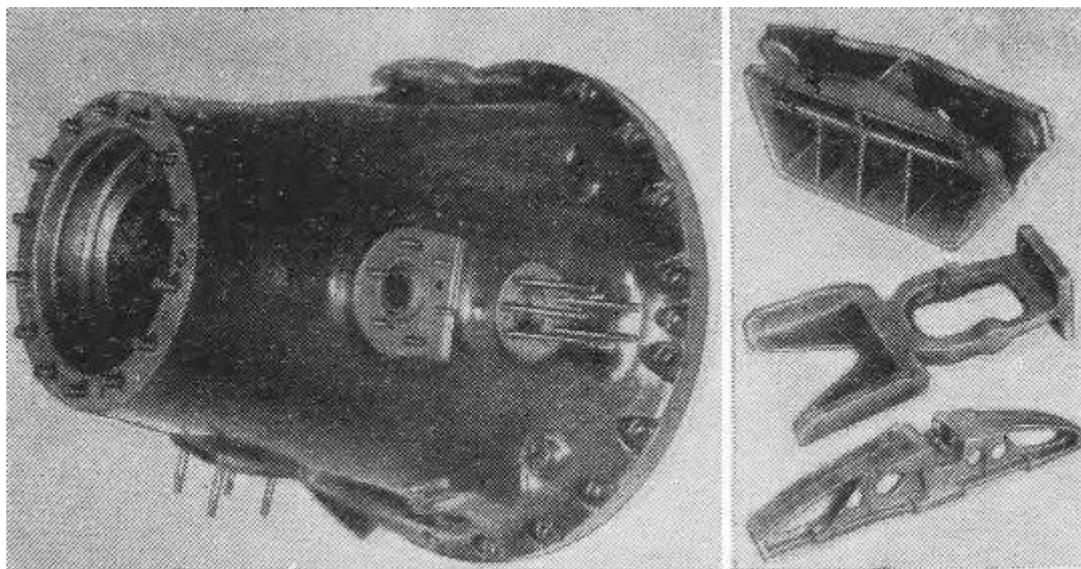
Детали самолетов и двигателей, отлитые из магниевых сплавов
